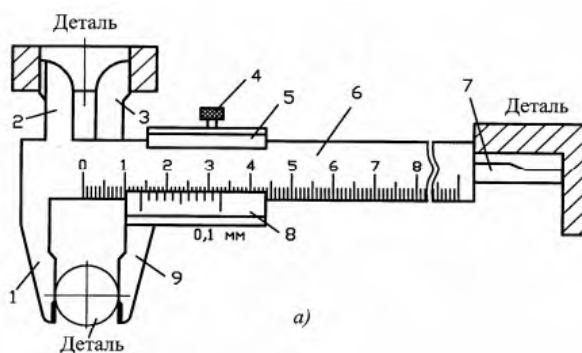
Штангенциркуль: схема измерения [2]
